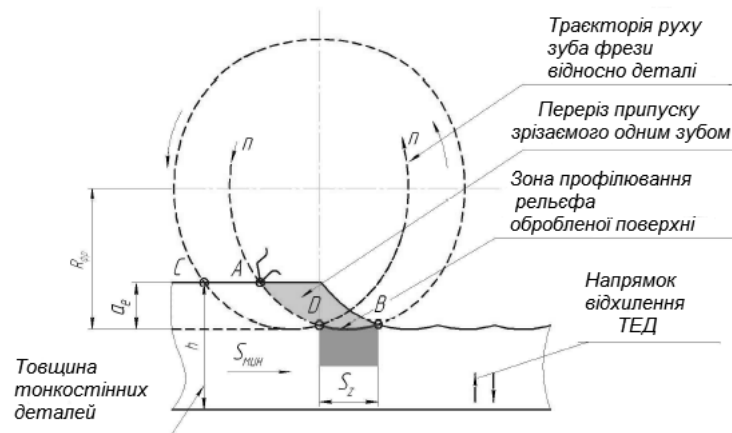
Формування профілю обробленої поверхні при попутному фрезеруванні ТЕД
